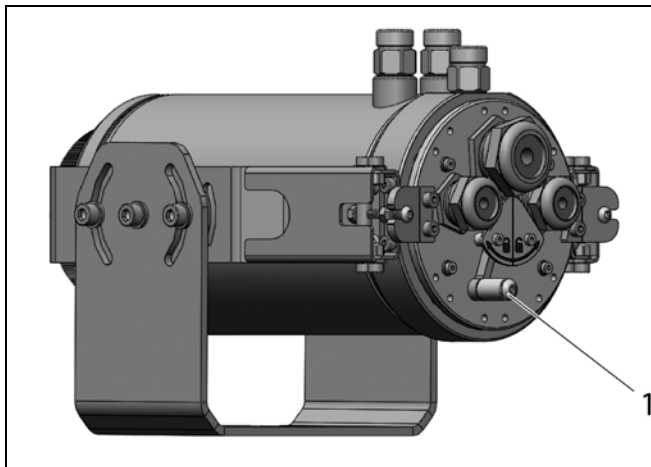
Rückansicht CoolingJacket mit Verriegelungshebel
